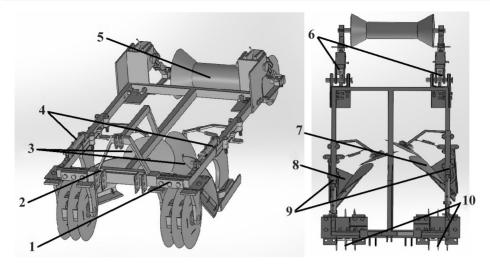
Общий вид лесного плуга для образования микроповышений: 1 — рама; 2 — навеска; 3 — сферические диски; 4 — гидроцилиндры; 5 — уплотняющий каток; 6 — пружины; 7, 8 — левооборачивающий и правооборачивающий лемешные корпуса соответственно; 9 — подвижные брусья; 10 — ножевые батареи
